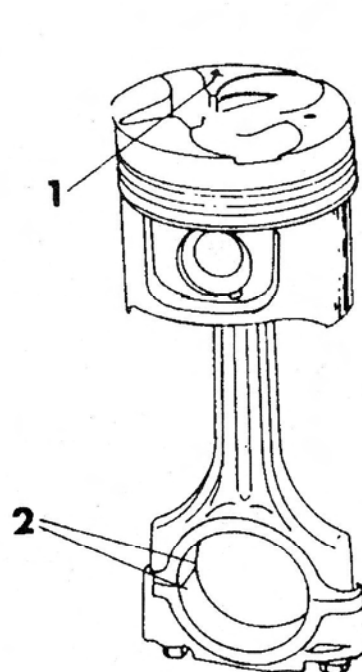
Стрелка (1) на днище поршня должна указывать на переднюю часть двигателя, если направляющие выступы (2) вкладышей шатунов находятся с левой стороны блока цилиндров.
